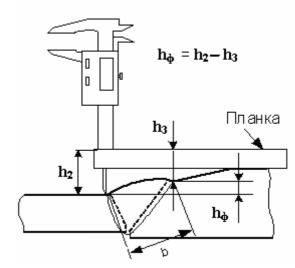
Схема измерения геометрии разнотолщинного сварного соединения
